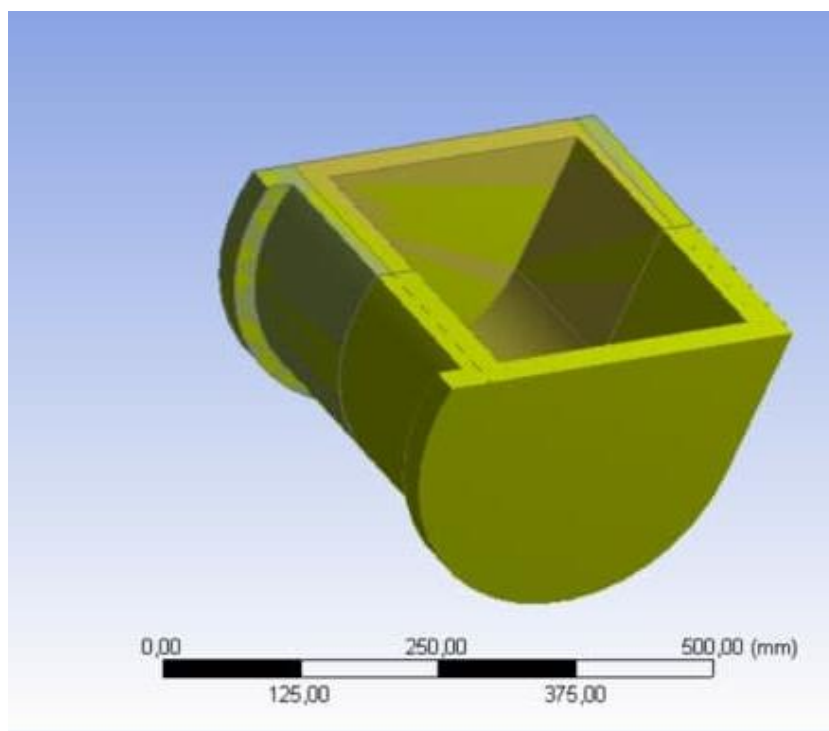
Підготовка модернізованої конструкції ковша елеватора для розрахунку в ANSYS
